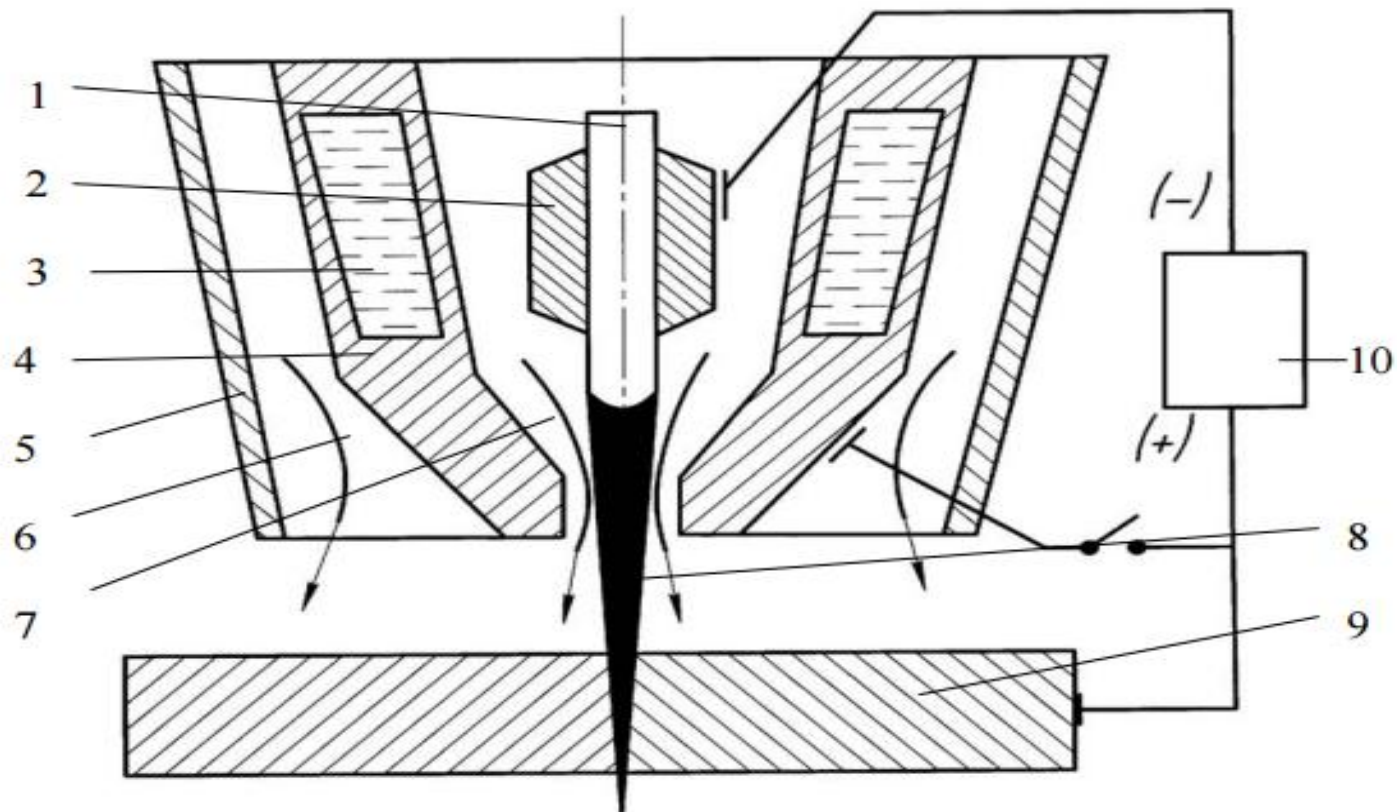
Схема плазмотрона – сварочной горелки для плазменной сварки и наплавки
